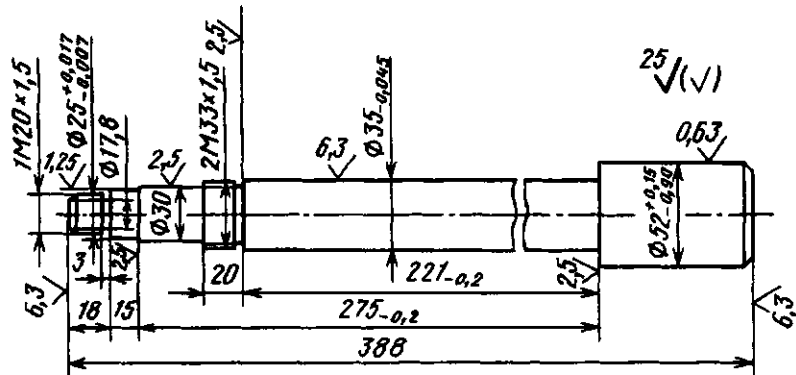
Рабочий чертеж вала, изготавливаемого ковкой на ВРКМ
